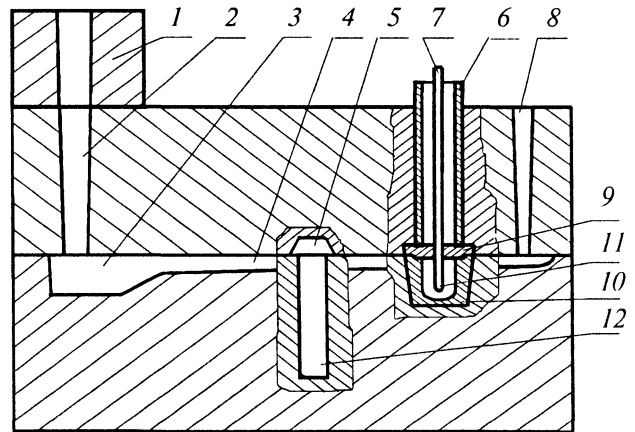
Поперечный разрез литейной формы: 1 — прибыльная надставка; 2 — главный наполнитель; 3 — реакционная камера; 4 — подводный канал; 5 — литейная прибыль; 6 — картонный экран термопар; 7 — керамический экран термопар; 8 — выпор; 9 — крышка образца; 10 — образец для термического анализа; 11 — термопары NiCr—NiAl; 12 — образец для исследования прочности
